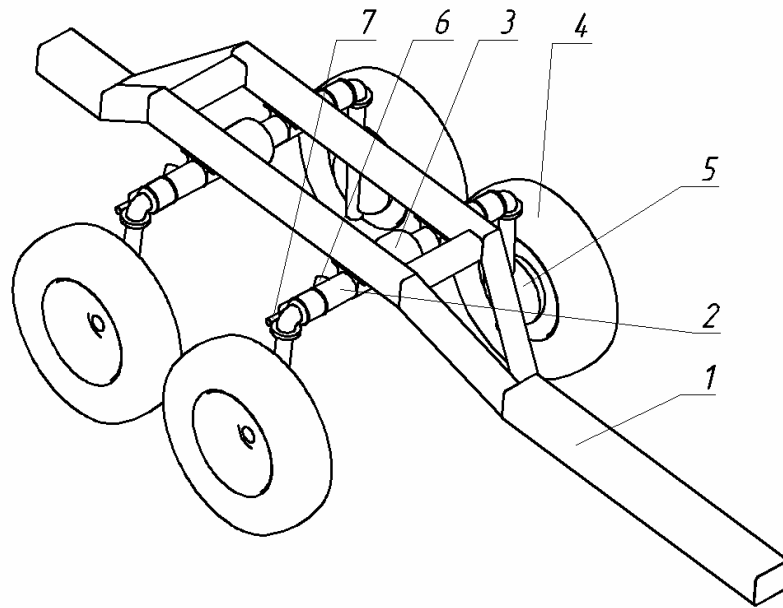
Компонка двухосного шасси установочного модуля: 1 – рама шасси; 2 – порталный мост; 3 – дифференциал; 4 – колесо; 5 – поворотная цапфа; 6 – гидромотор привода поворота колес; 7 – червячная передача
